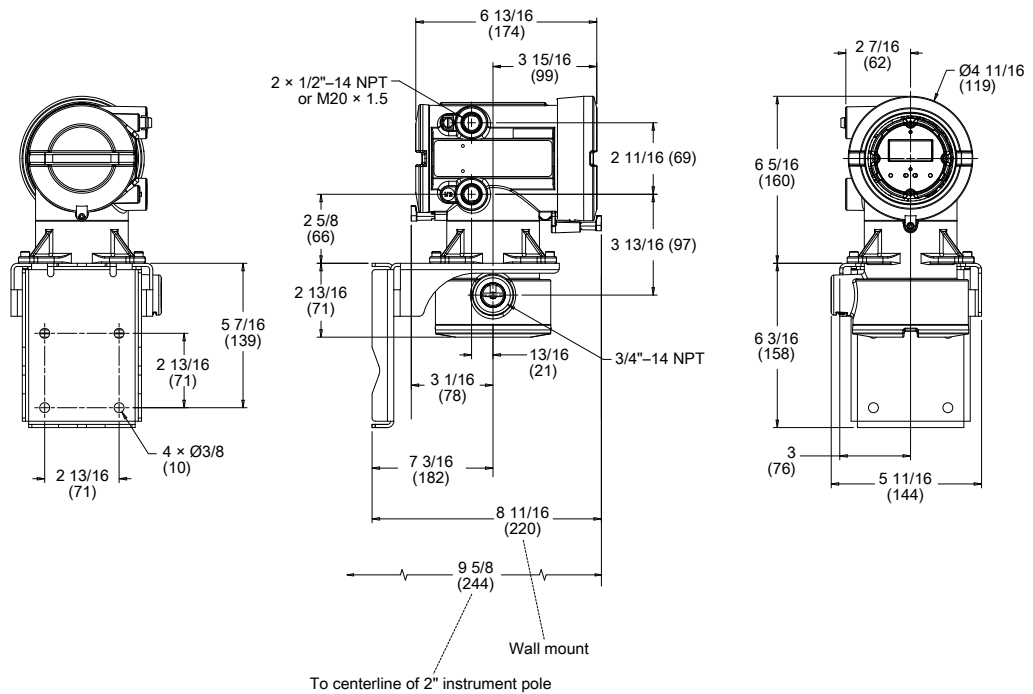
Dimensiones del transmisor de montaje remoto de 4 y 9 hilos (carcasa de acero inoxidable)
